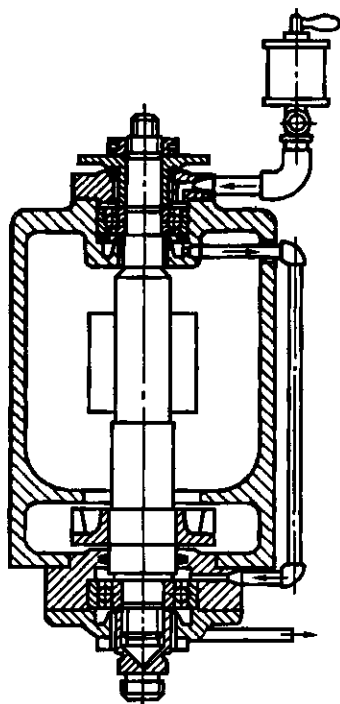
Смазка подшипников вертикального вала с помощью масленки с запорной иглой
